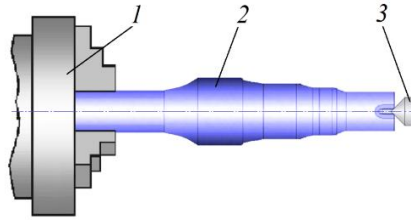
Схема закрепления основного вала на токарном станке: 1 – патрон; 2 – основной вал; 3 – подвижный центр задней бабки
